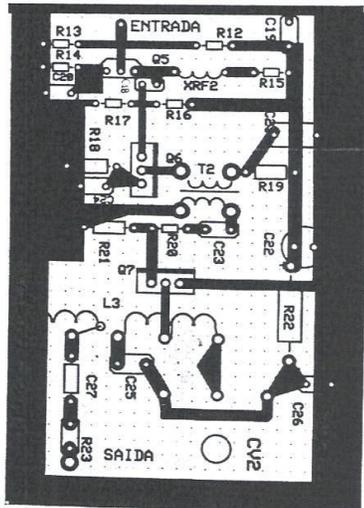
PLACA DE FIXAÇÃO IMPRESSA DO EXCITADOR
